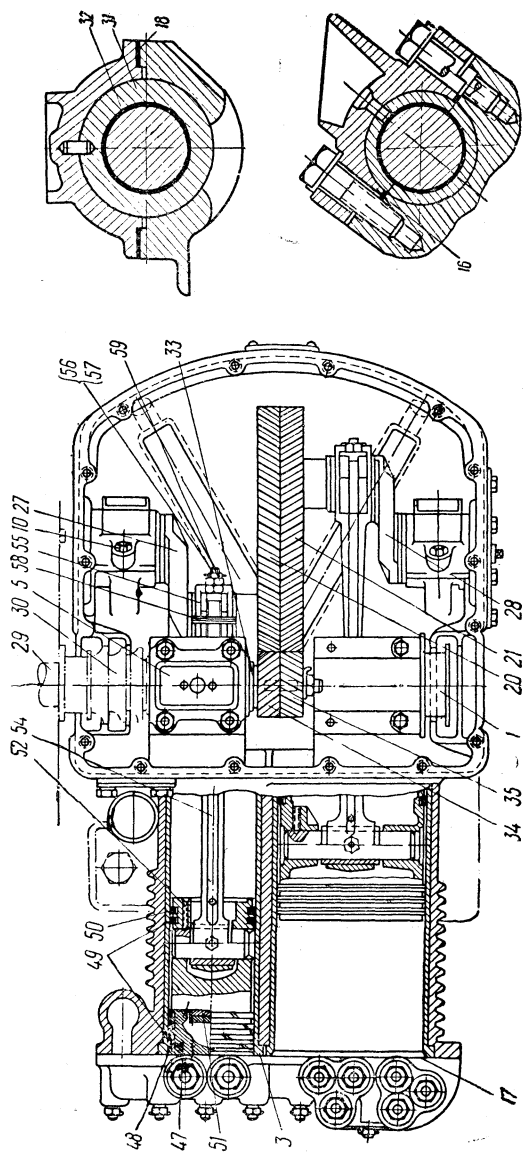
Мотор-компрессор усл. № 9-500 (вид сверху в разрезе по цилиндрам, по подшипнику вала мотора и по подшипнику коленчатого вала)
